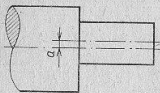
Zkřivení vnitřního kroužku ložiska způsobené obrobením čela osazení
